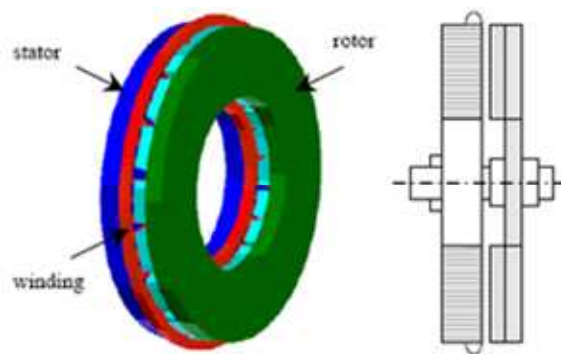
Machine à flux axial 1 stator / 1 rotor. [AYD 04]
